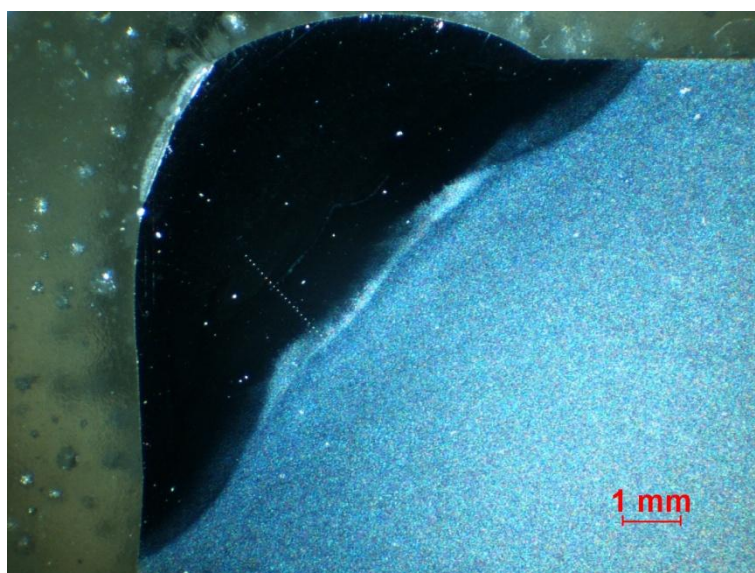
Makrostruktura návaru u vzorku č. 2
